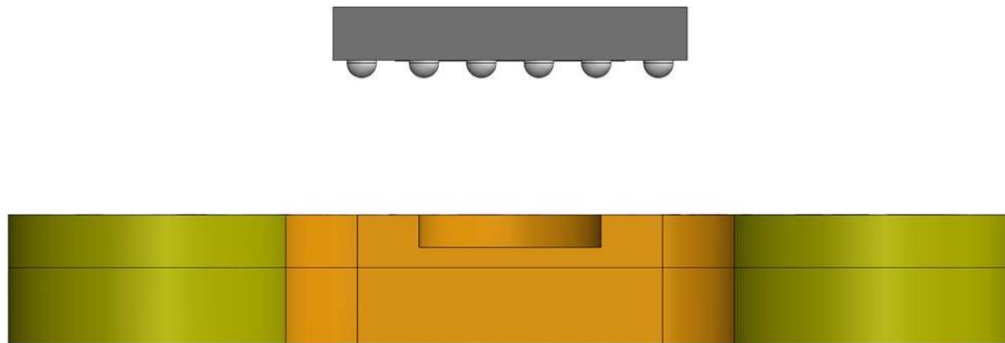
Vista Frontal de microcircuito BGA y socket de prueba
